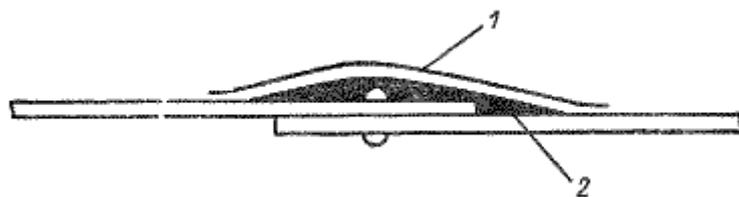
Глухая заделка клепаных соединений наружной обшивки шпатлевочными или клеевыми массами.
